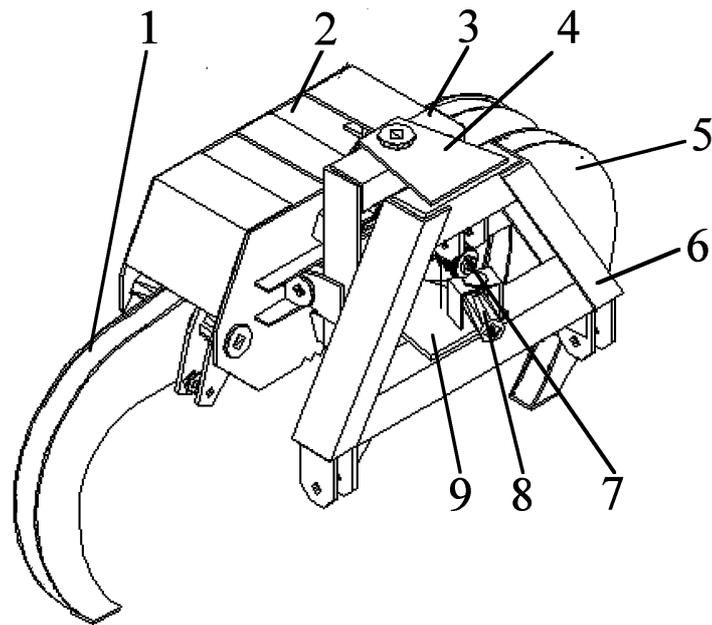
Общий вид трелевочного захвата: 1 – клык ведомый; 2 – корпус захвата; 3 – крестовина; 4, 9 – кронштейны; 5 – клык ведущий; 6 – звено навесное; 7 – пружинный узел; 8 – установитель;
